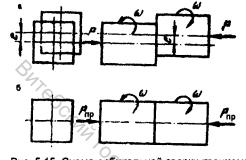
Схема орбитальной сварки трением: а – стадия нагрева: б – стадия проковки
